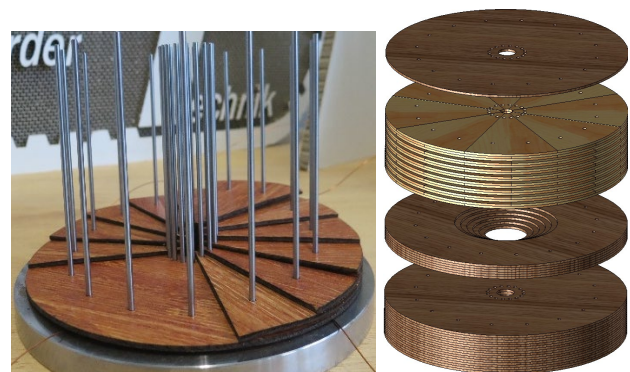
Sortiervorrichtung mit eingelegten Furnierscheiben und Kreissegmenten (links) und Lagenaufbau (rechts)
